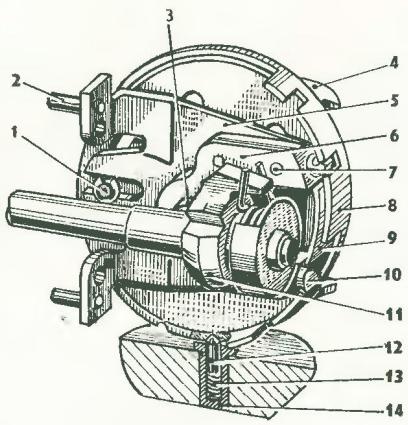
Механизм переключения передач: 1 — ось вилки; 2 — установочный штифт; 3 — ось корпуса собачек; 4 — вилка; 5 — основание механизма; 6 — корпус собачек; 7 — стопорный штифт; 8 — диск; 9 — утопитель собачек; 10 — собачка; 11 — поводок валика; 12 — корпус фиксатора; 13 — пружина; 14 — фиксатор.
